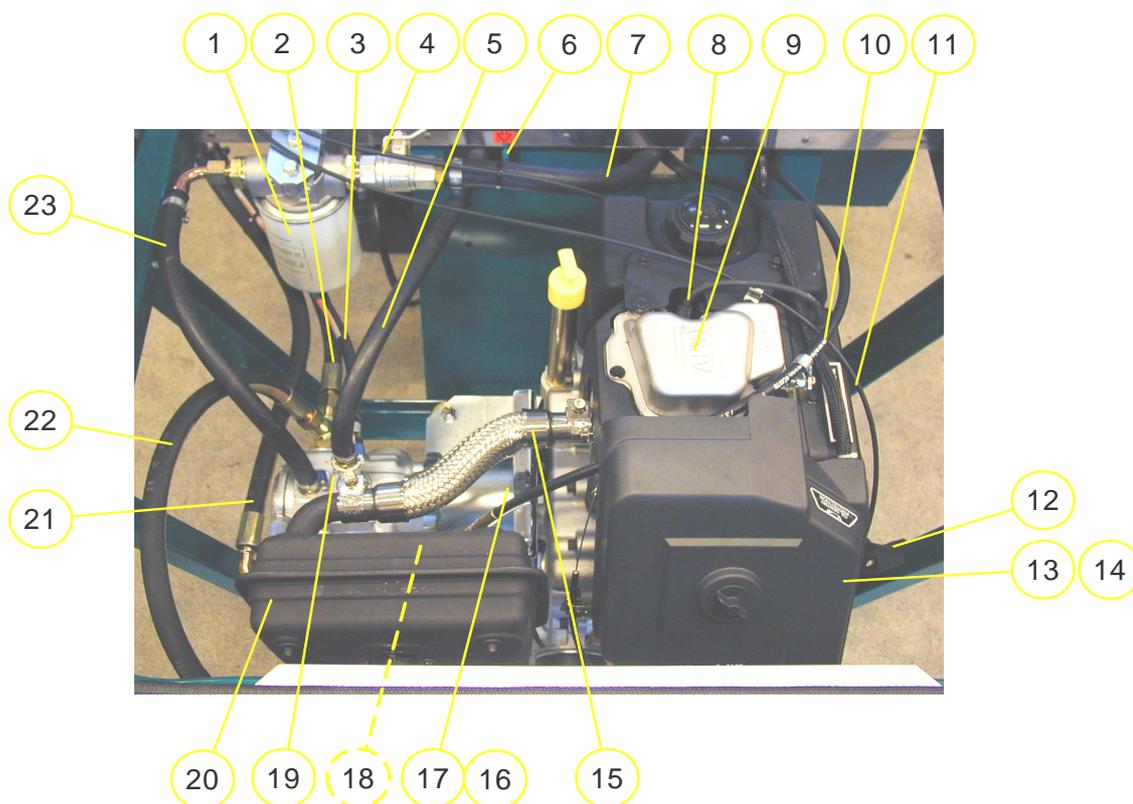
Emplacement moteur, vue de haut, Kohler 15 CV
